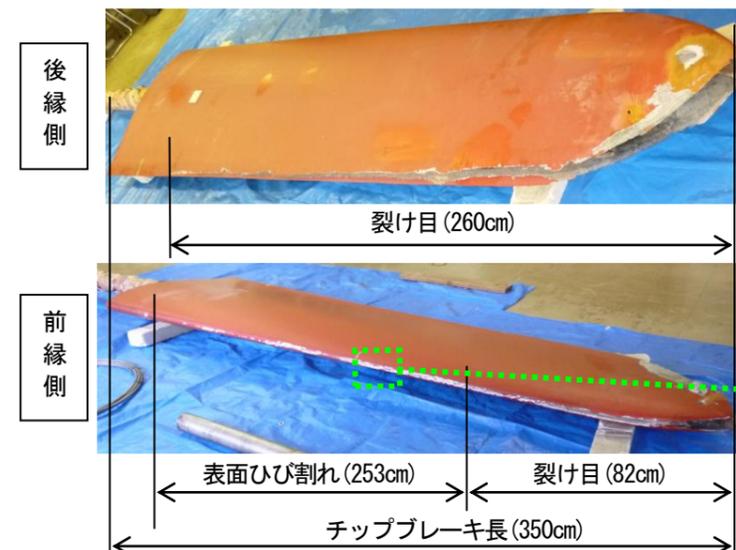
チップブレーキの裂け目および表面ひび割れ状況
